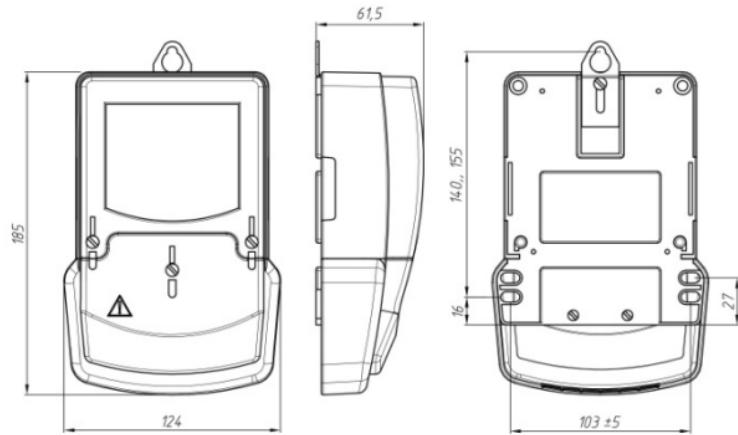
Габаритные и установочные размеры счетчика в корпусе S10
